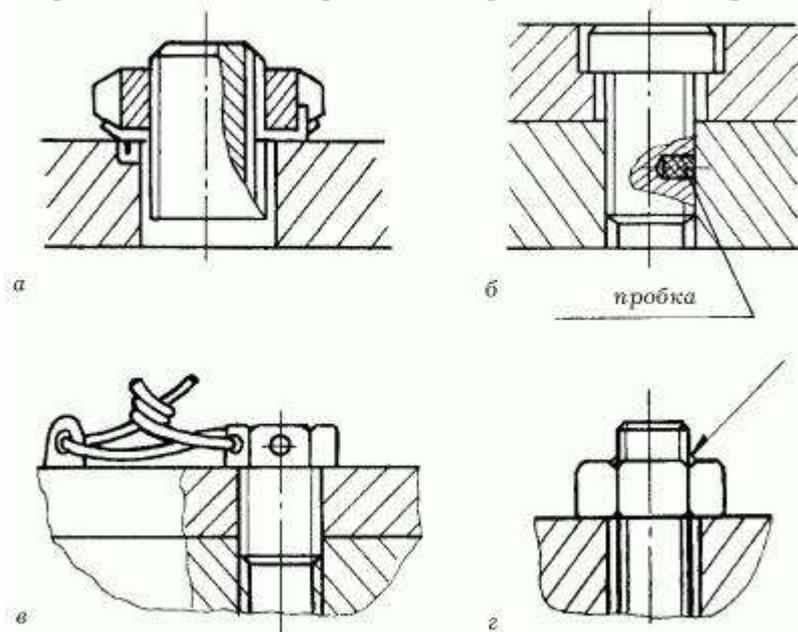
Способы стопорения резьбовых соединений: а – стопорной шайбой; б – пробкой; в – проволокой; г – сваркой или накерниванием.
